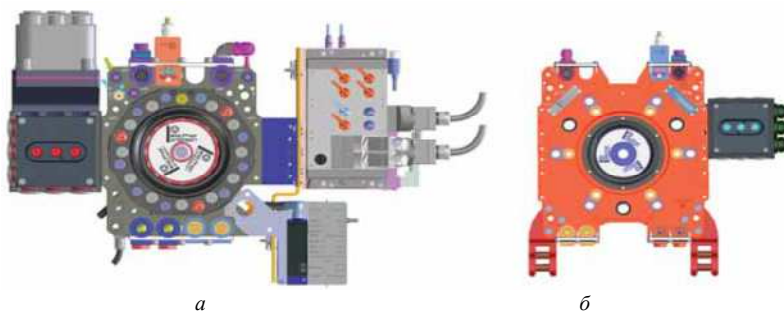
Конструкция входного (а) и выходного (б) фланца УАСРО TOOL MASTER 500 для промышленных роботов: тип 91489
